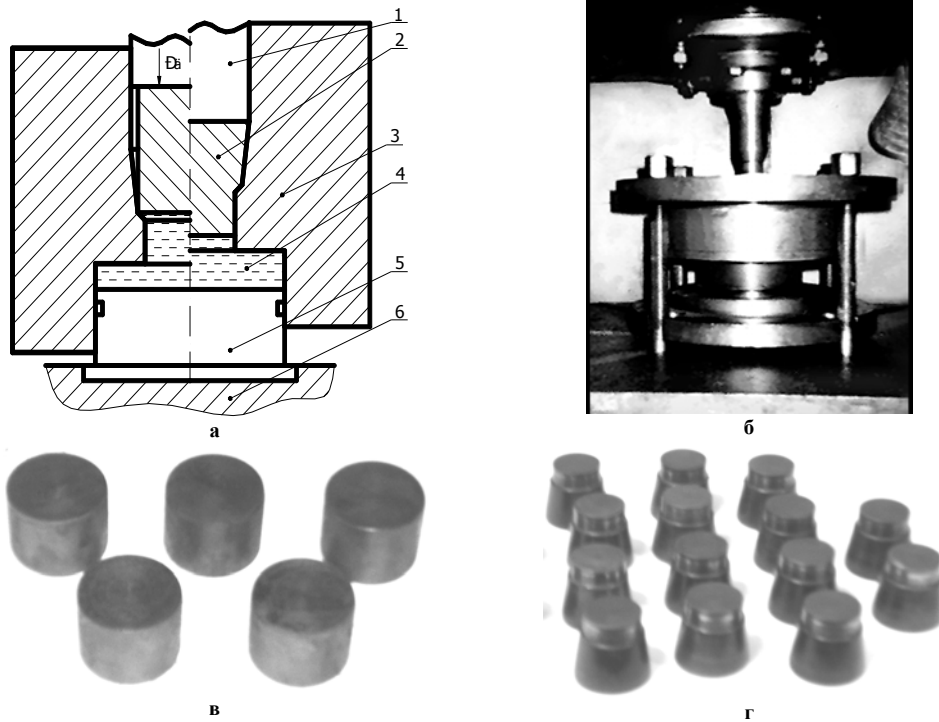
Схема видавлювання заготовок штемпелів (а), виробничий штамп для видавлювання (б), вихідні заготовки (в) та заготовки після видавлювання (г)
